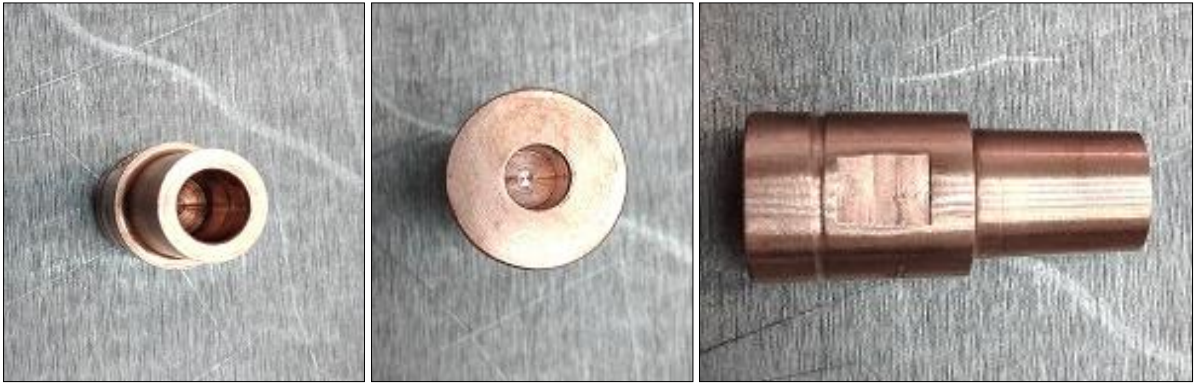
Vista anterior, posterior y lateral de un electrodo superior apto para soldadura por proyección.
